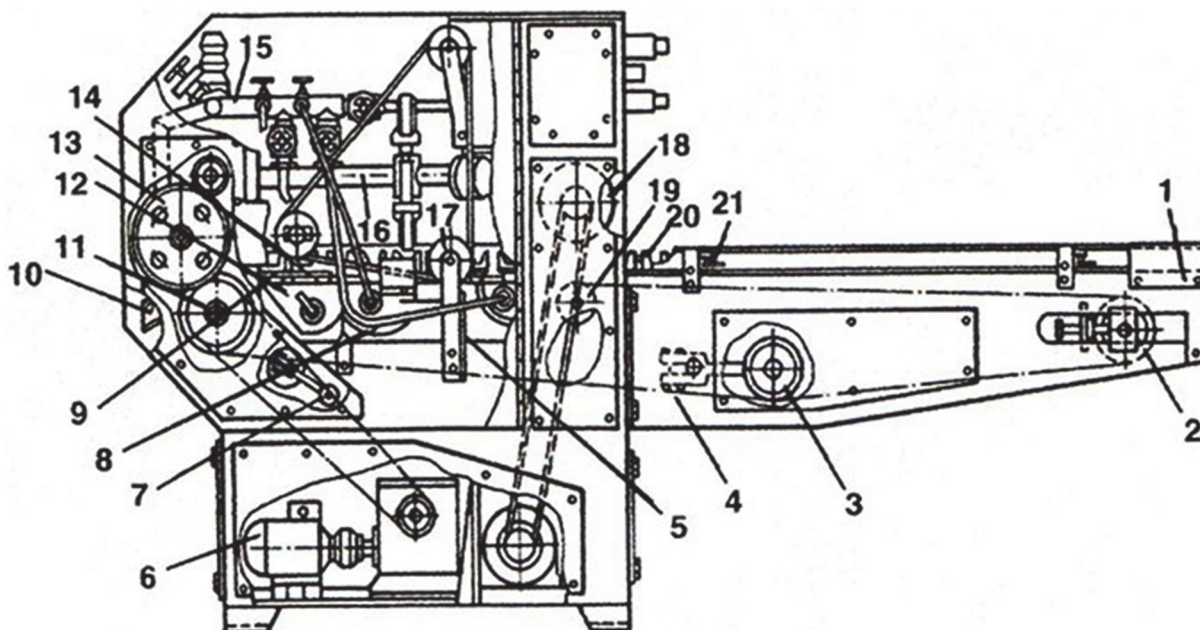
Схема устройства машины НЗ-ИРЗ
